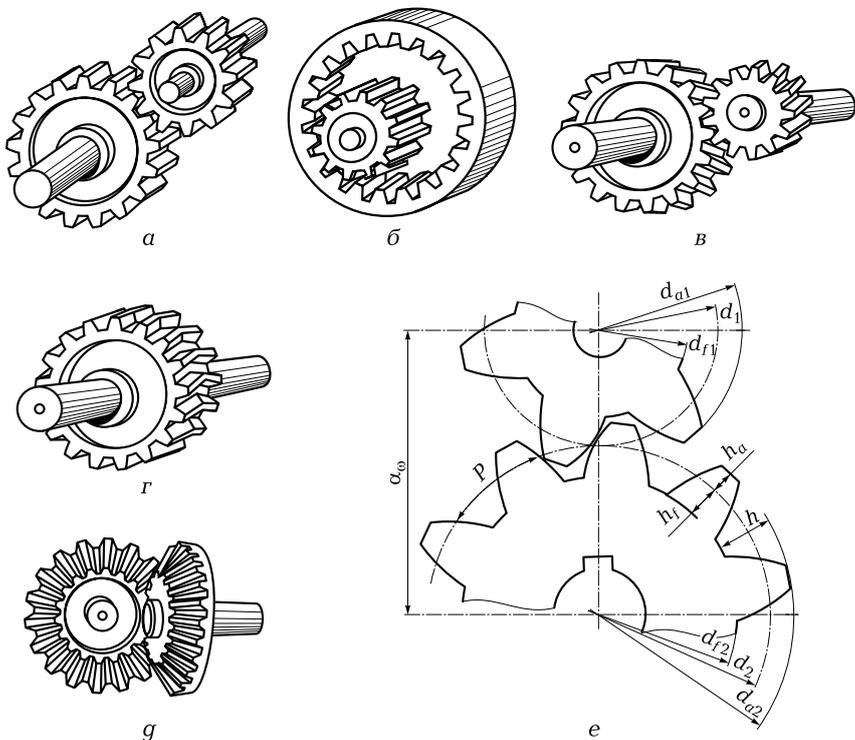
Зубчатые передачи и элементы зубчатого колеса:
